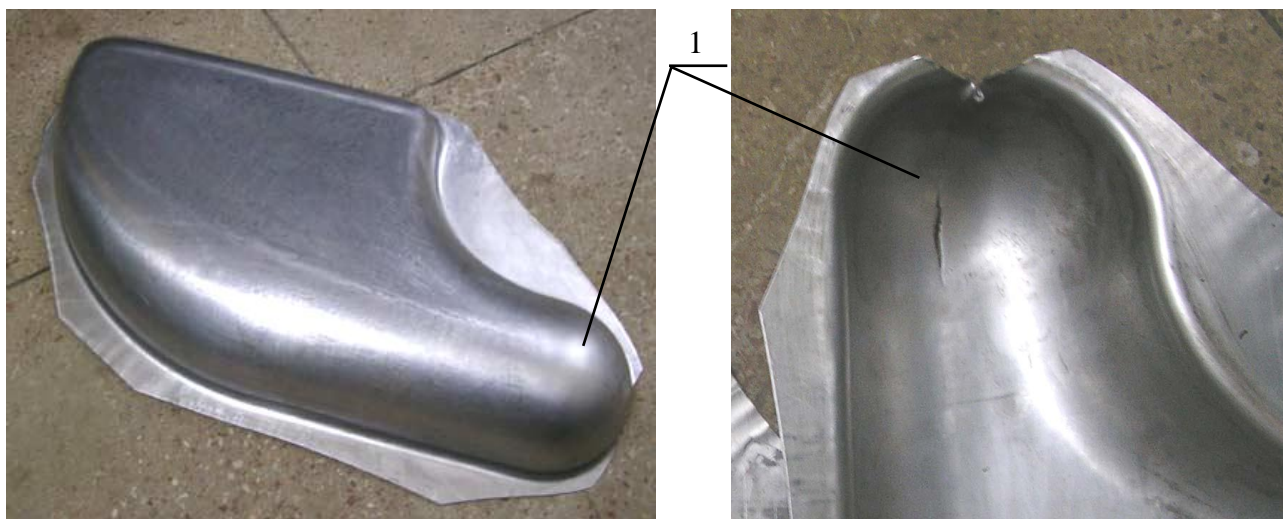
Общий вид штампованного полуфабриката детали «полупатрубок» из алюминиевого сплава АМг6М из листа толщиной 2 мм: 1 – технологический участок заготовки, использованный для изготовления образцов
